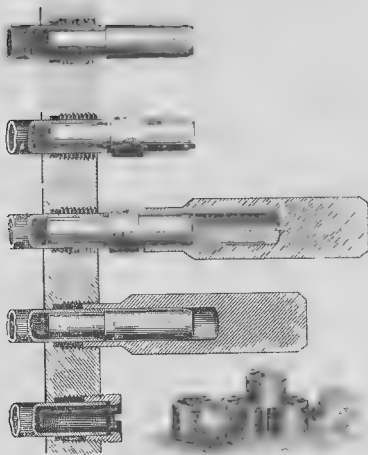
Набивка сальников готовыми кольцами посредством специальных приспособлений.
